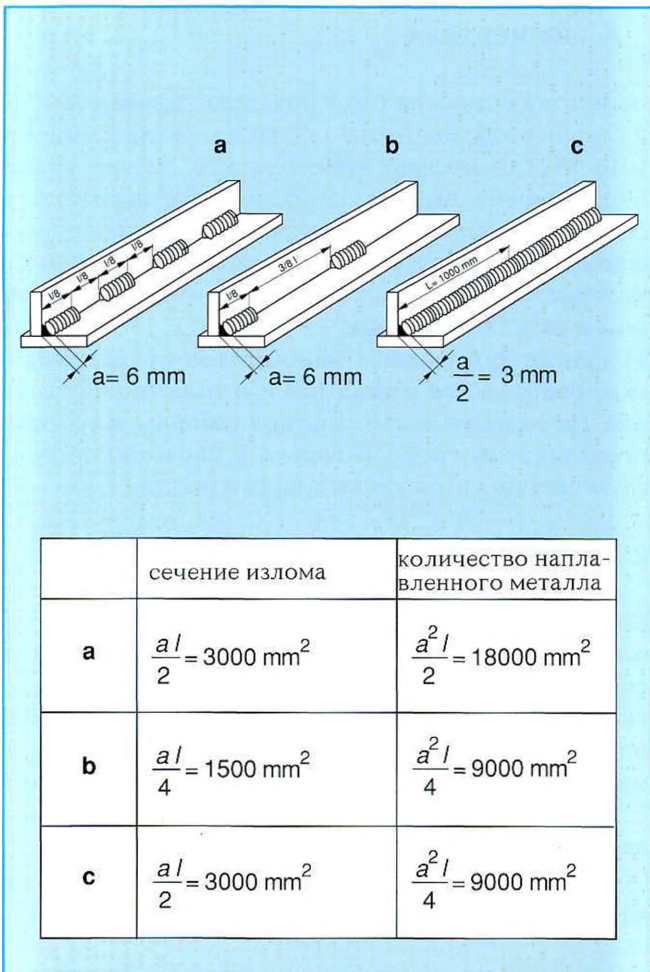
Сравнение угловых швов, полученных сваркой прерывистым швом и сваркой напроход
